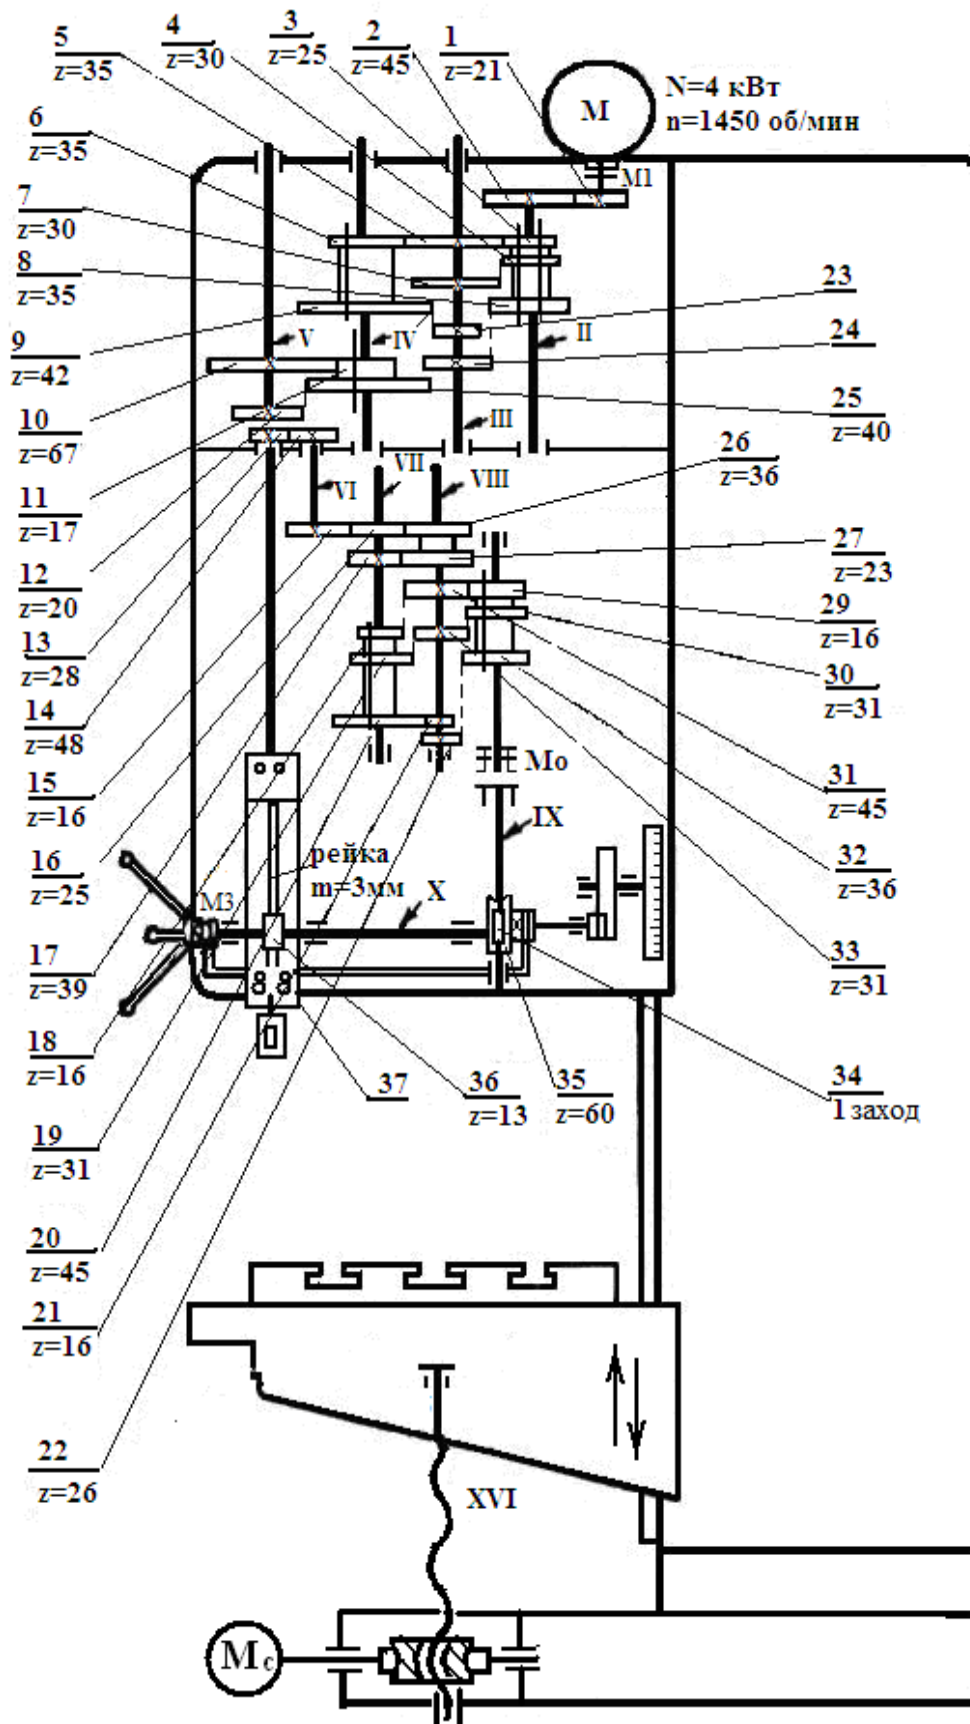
Кинематическая схема вертикально-сверлильного станка 2Н18
